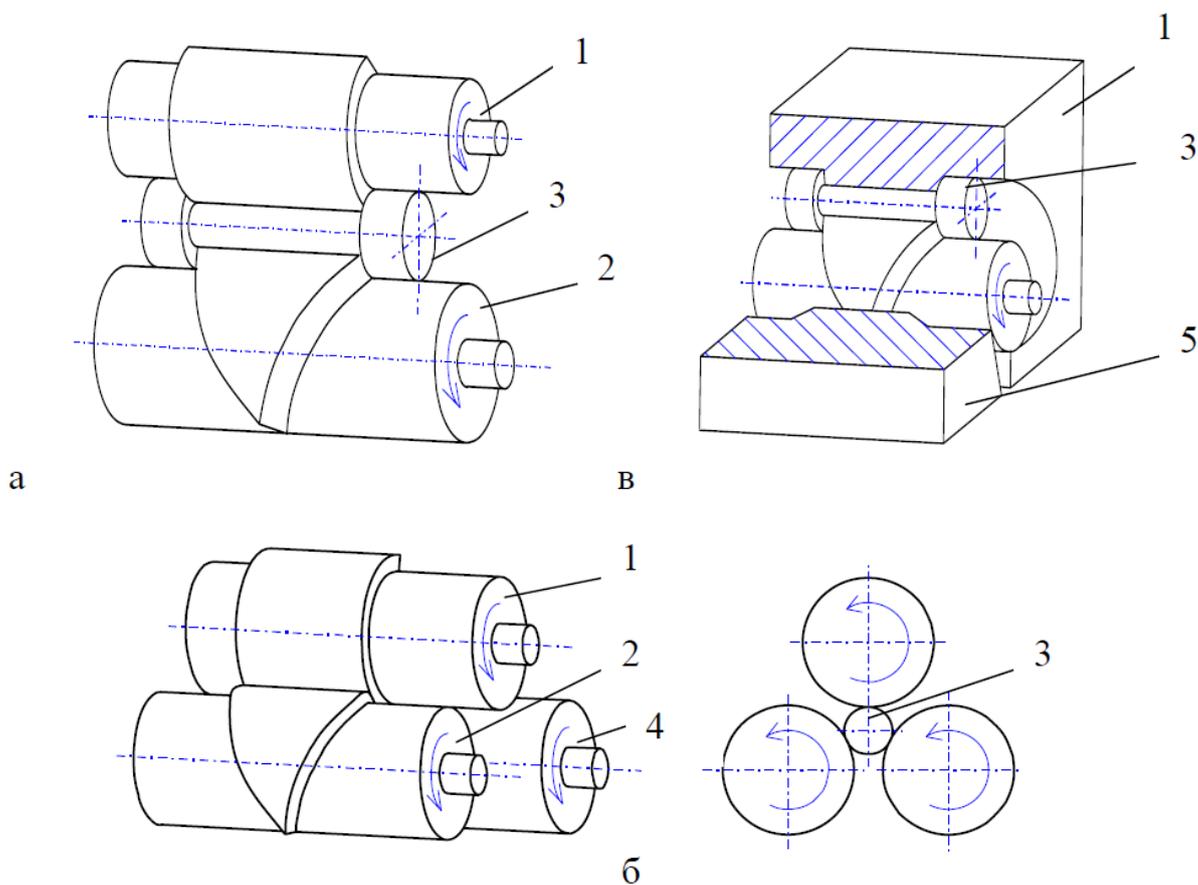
Загальні схеми поперечно-клинової прокатки:
